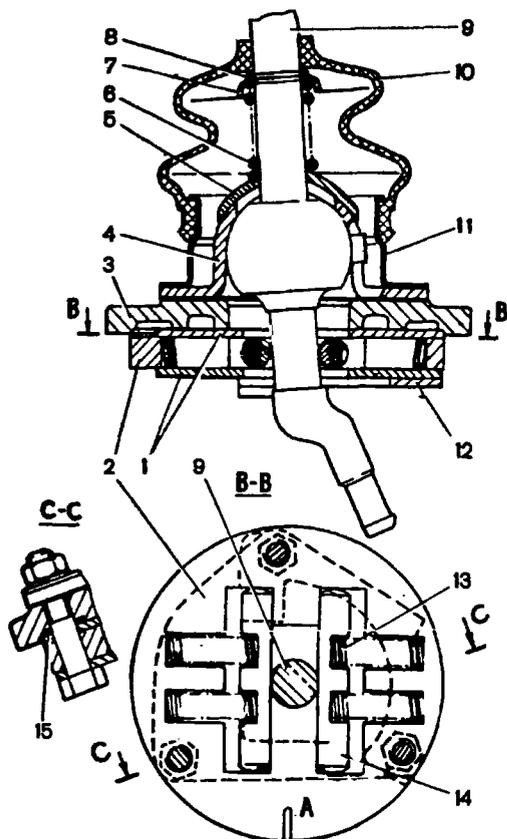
Механизм выбора передач: 1 - шайба направляющей пластины; 2 - направляющая пластина; 3 - корпус рычага переключения передач; 4 - шаровая опора; 5 - сферическая шайба; 6 - пружина; 7, 8 - стопорные кольца; 9 - рычаг переключения передач; 10 - защитный чехол; 11 - фланец; 12 - блокировочная пластина заднего хода; 13 - пружина; 14 - направляющая планка; 15 - уплотнительное кольцо; А - риска
